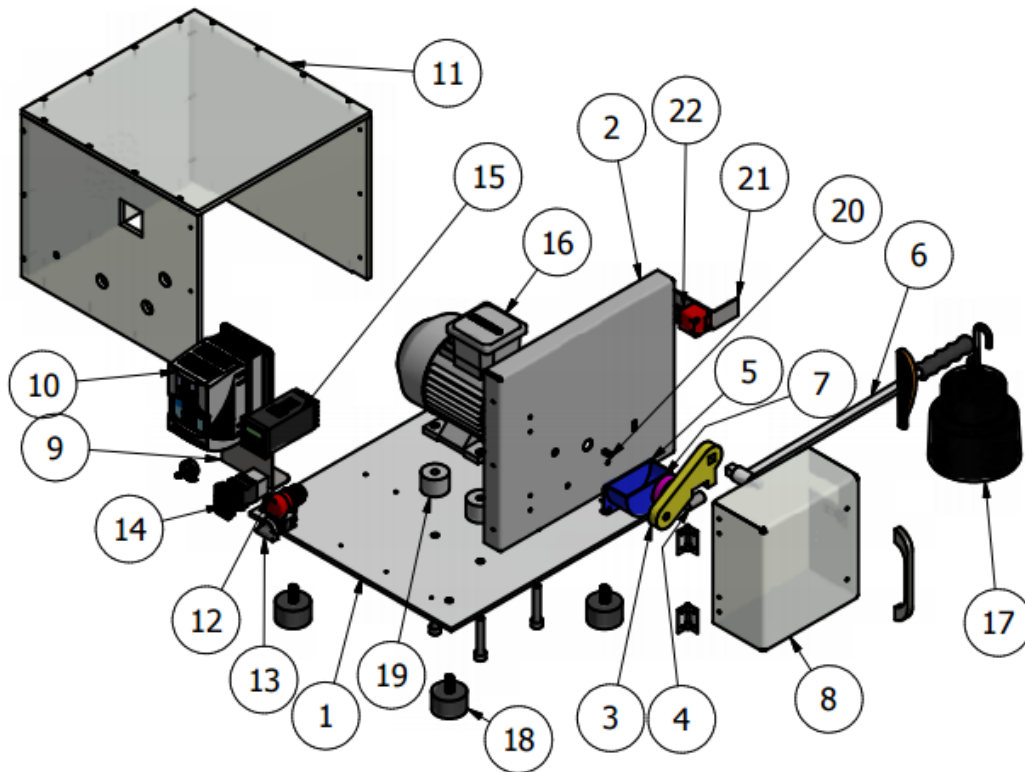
Vista explodida da máquina. Fonte: Autores.
